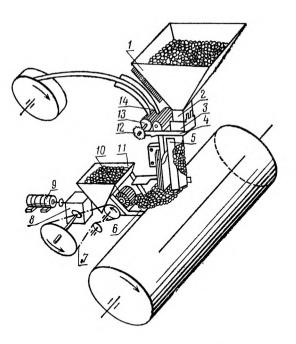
Схема флюсодозирующего и шлакоудерживающего устройства установки для наплавки валов ленточным электродом:
